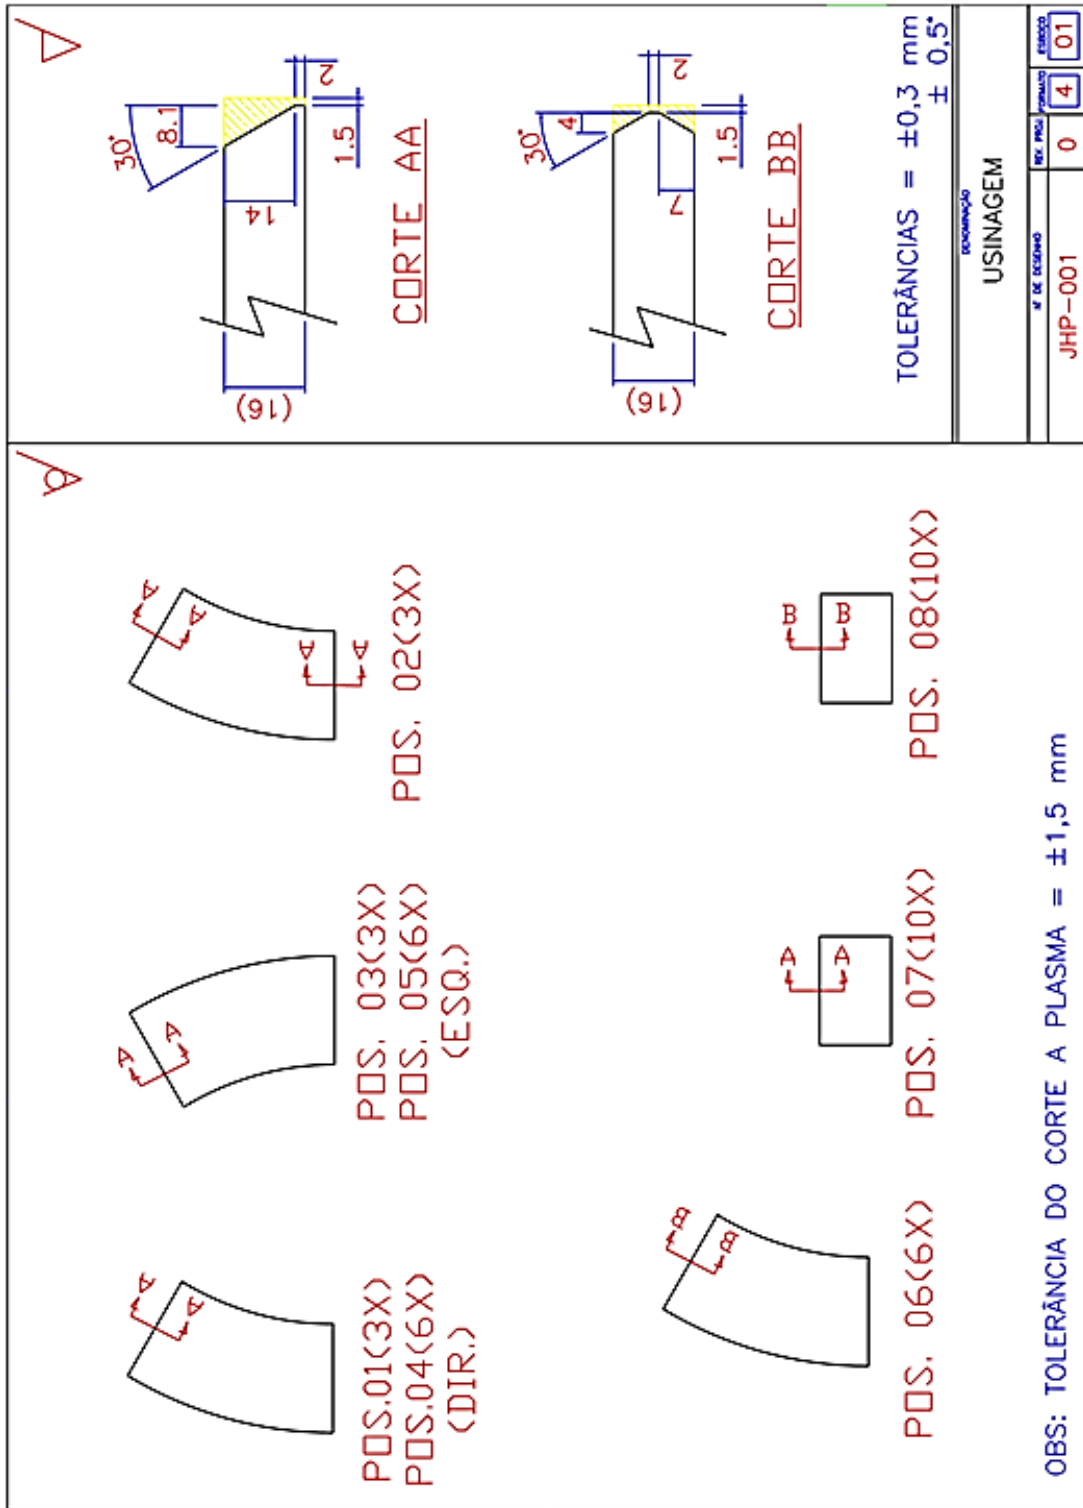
Desenho de preparação e usinagem dos corpos de prova.
